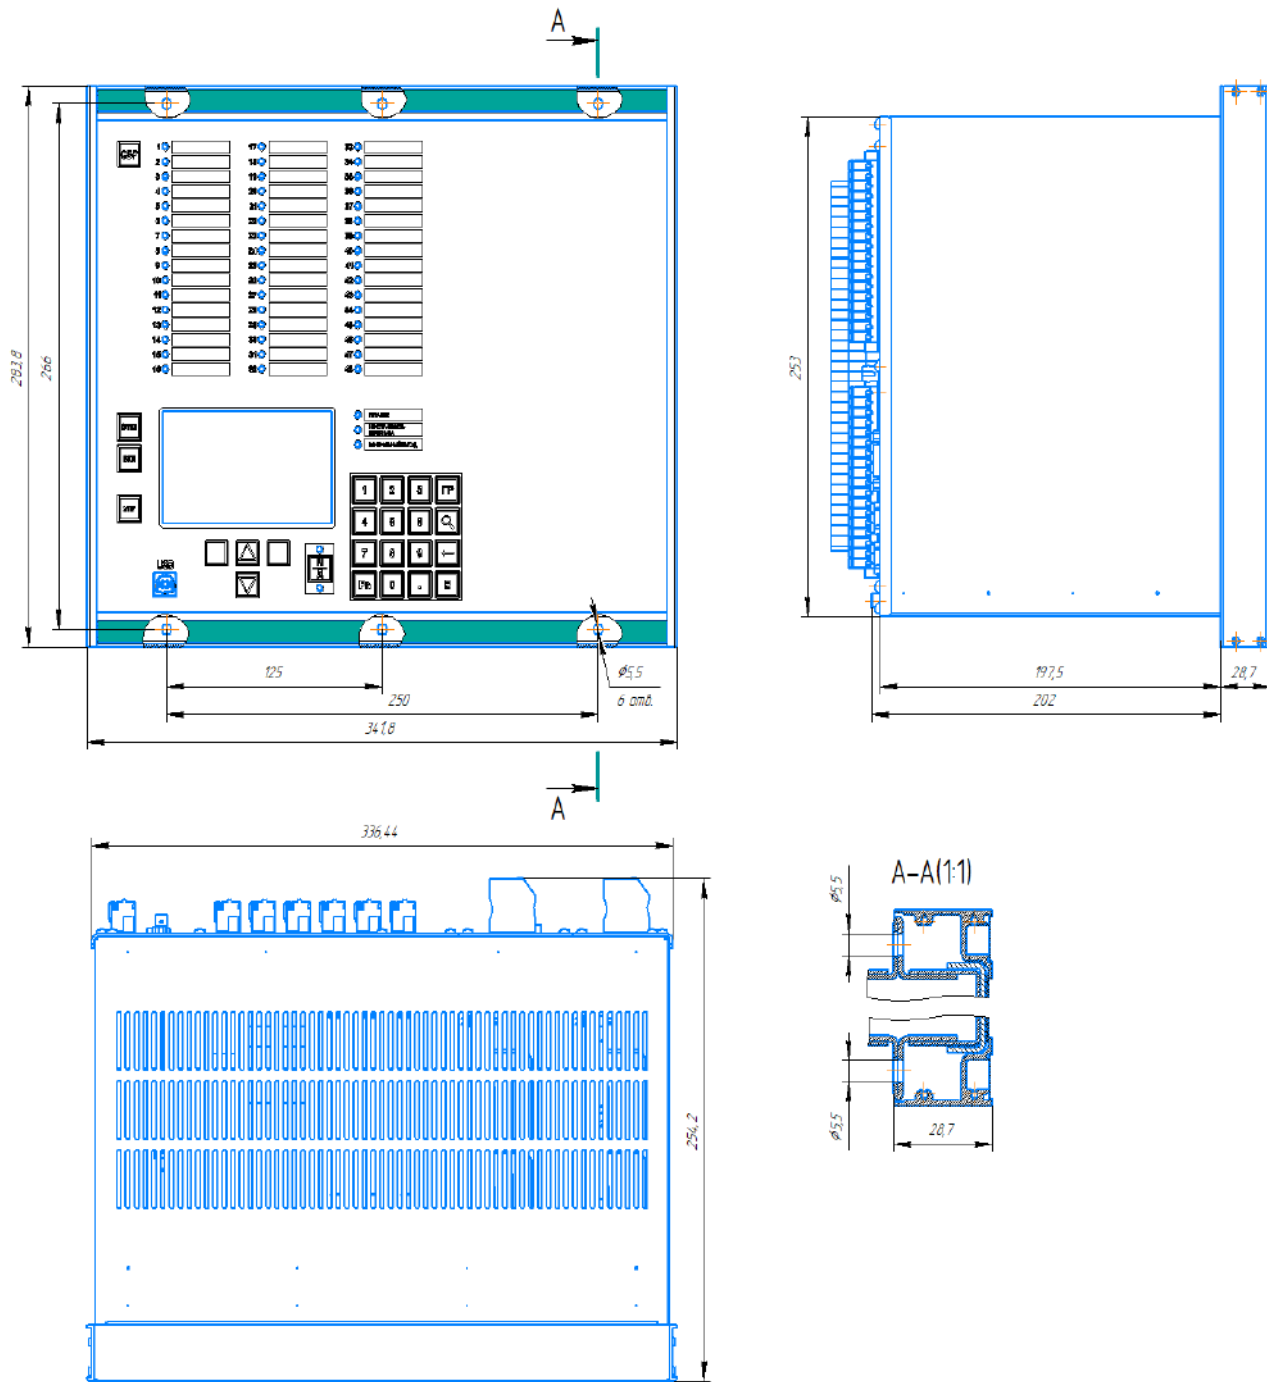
Габаритные и установочные размеры терминала БЭ2704 308
